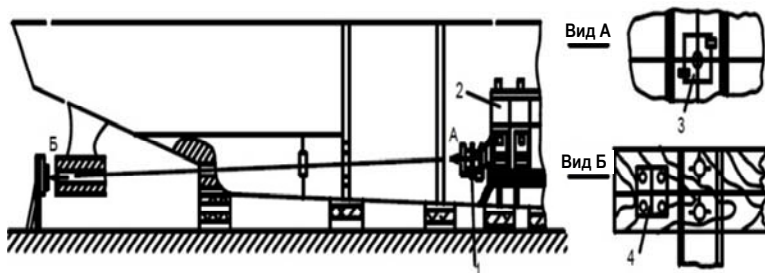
Схема центрирования главного двигателя в корпусе судна:
